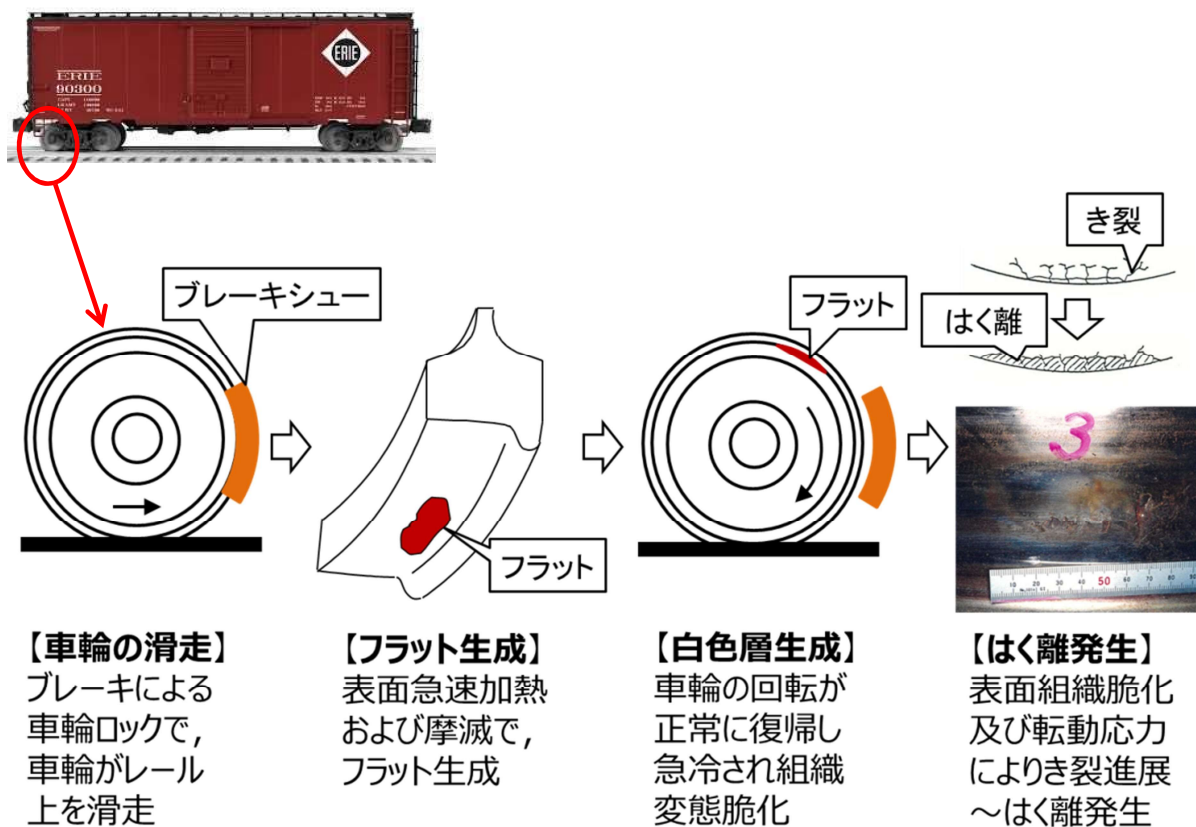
フラットはく離 (Spalling) 発生プロセス
